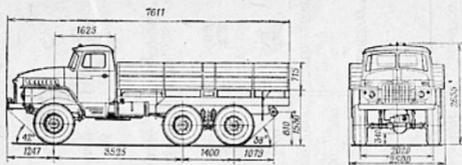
Габаритный чертеж автомобиля Урал-375Н
